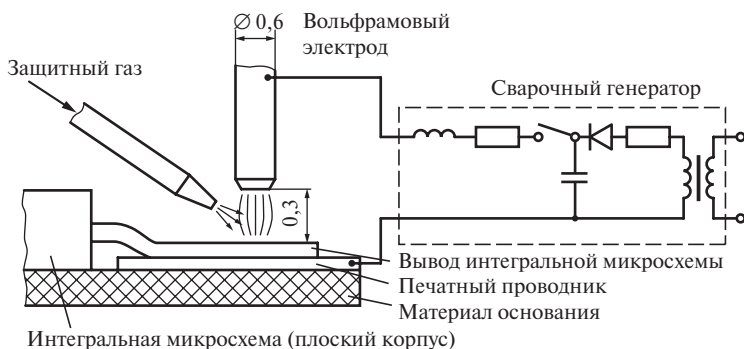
Принцип точечной электродуговой сварки
